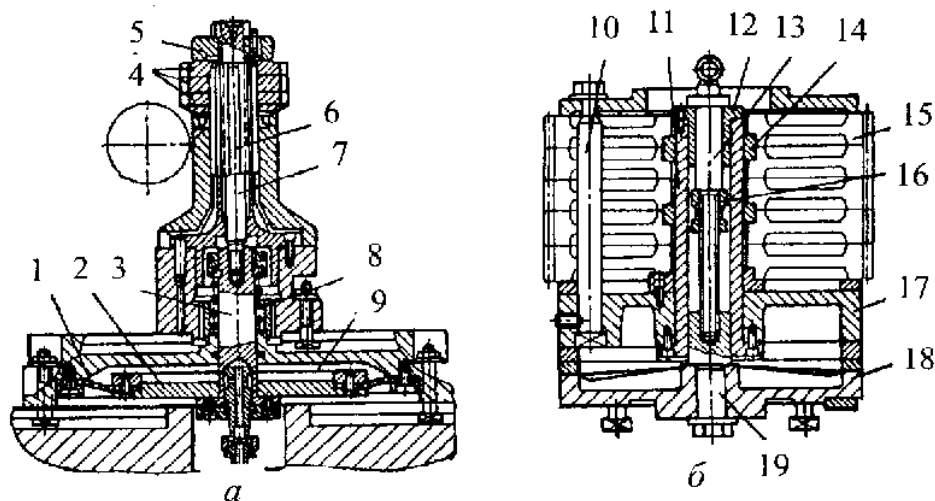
Пристрої до зубофрезерних верстатів
